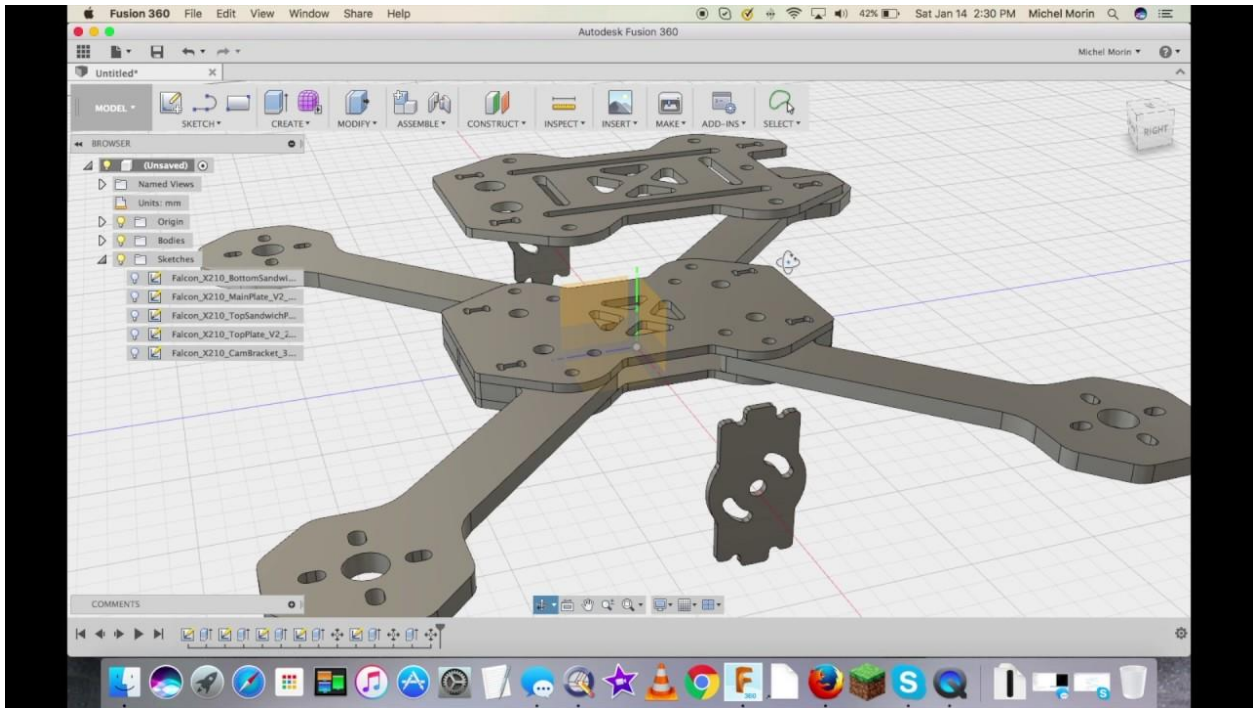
3D-модель корпусу БПЛА,
